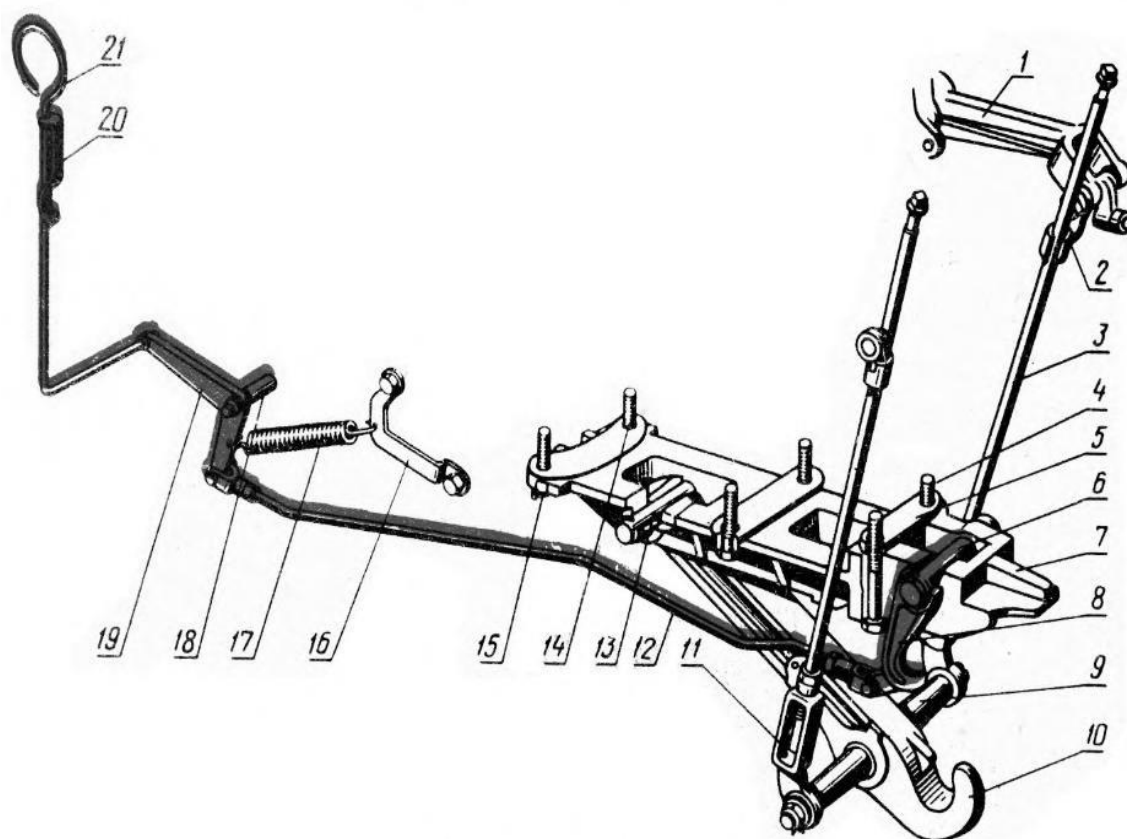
Деталі конструкції гідрофікованого гака трактора: 1 – зовнішній важіль навішування; 2 – серга; 3 – підймальна тяга; 4 – болт; 5 – регулювальна прокладка; 6 – вісь захоплення; 7 і 16 – кронштейни; 8 – захоплювальний пристрій; 9 – вісь гака; 10 – гак; 11 – гайка тяги; 12 – тяга; 13 – вісь; 14 – болт; 15 – відгинальна шайба; 17 – пружина; 18 – вісь важеля; 19 – важіль; 20 – фіксатор; 21 – рукоятка
